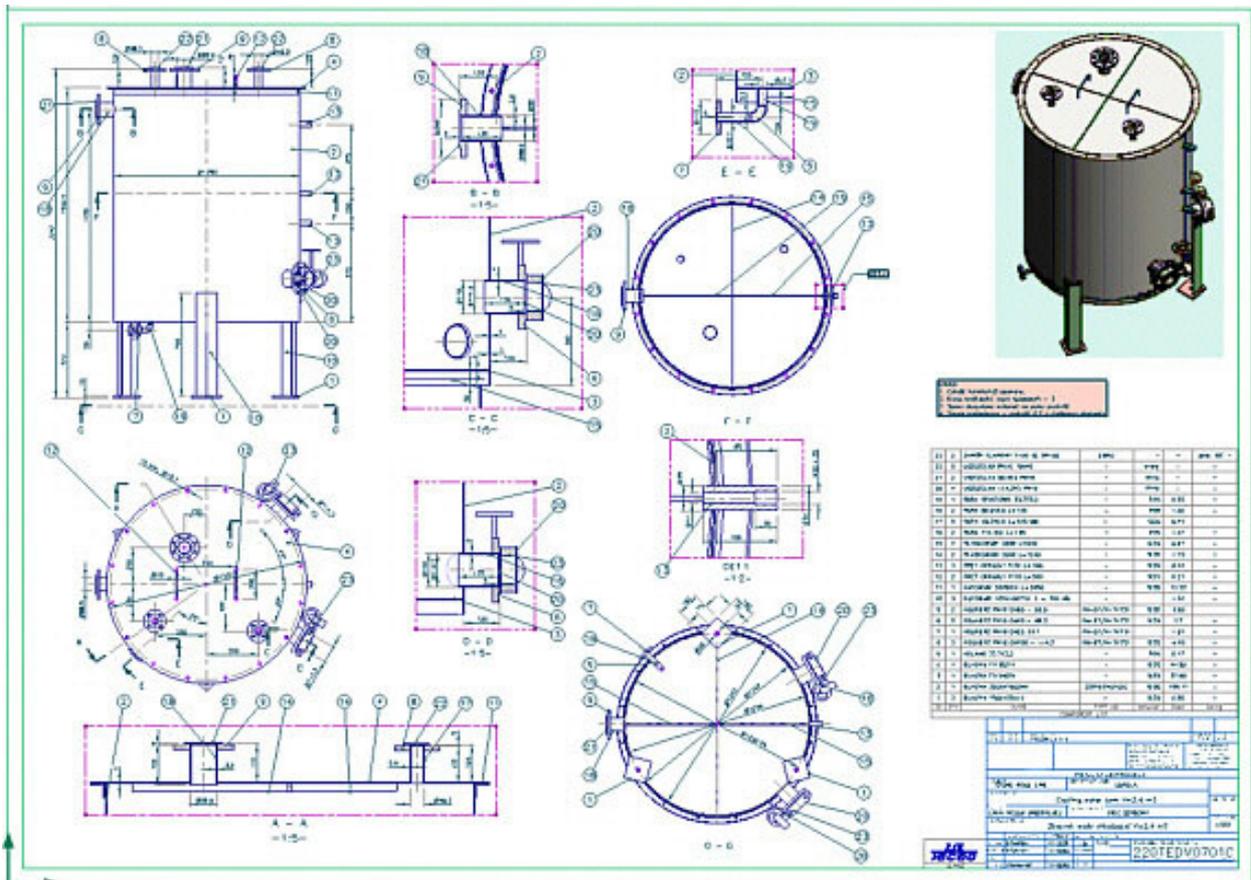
Lučka oprema konstruiranja u paketu CATIA
